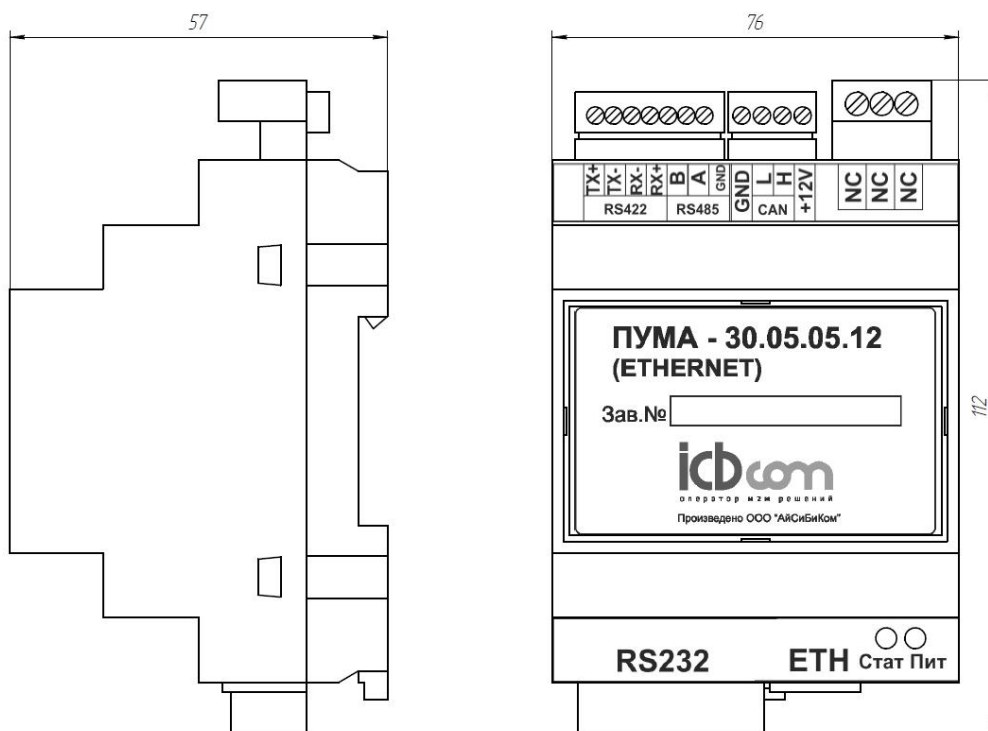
Внешний вид контроллера версии «ПУМА-30.05.05.12»
